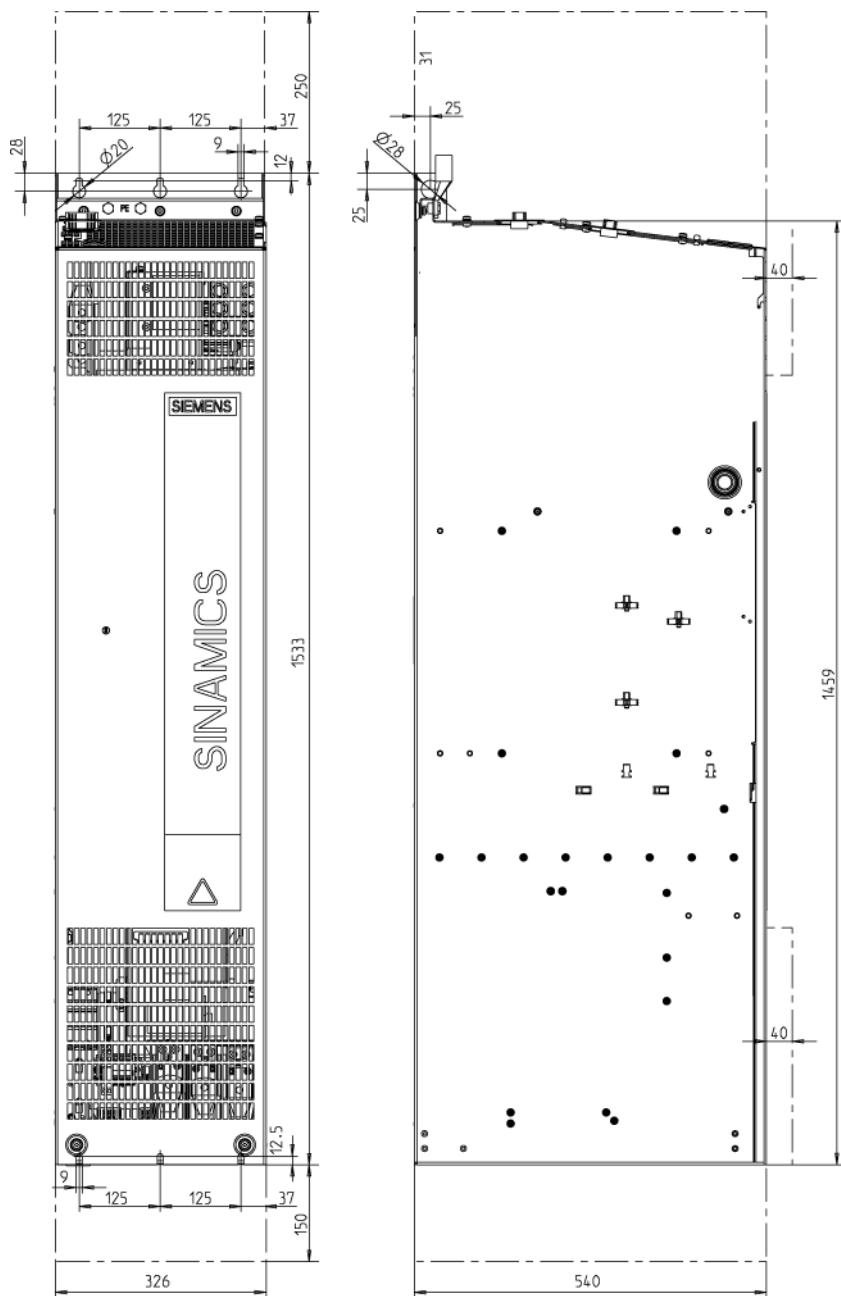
GX 型ALM的外形尺寸图 正视图和侧视图
